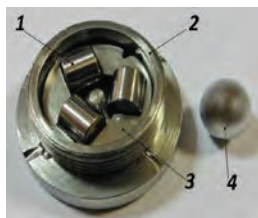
Оправка в сборе (крышка удалена): 1 - ролик; 2 – корпус оправки; 3 – сепаратор, 4 – шарик
